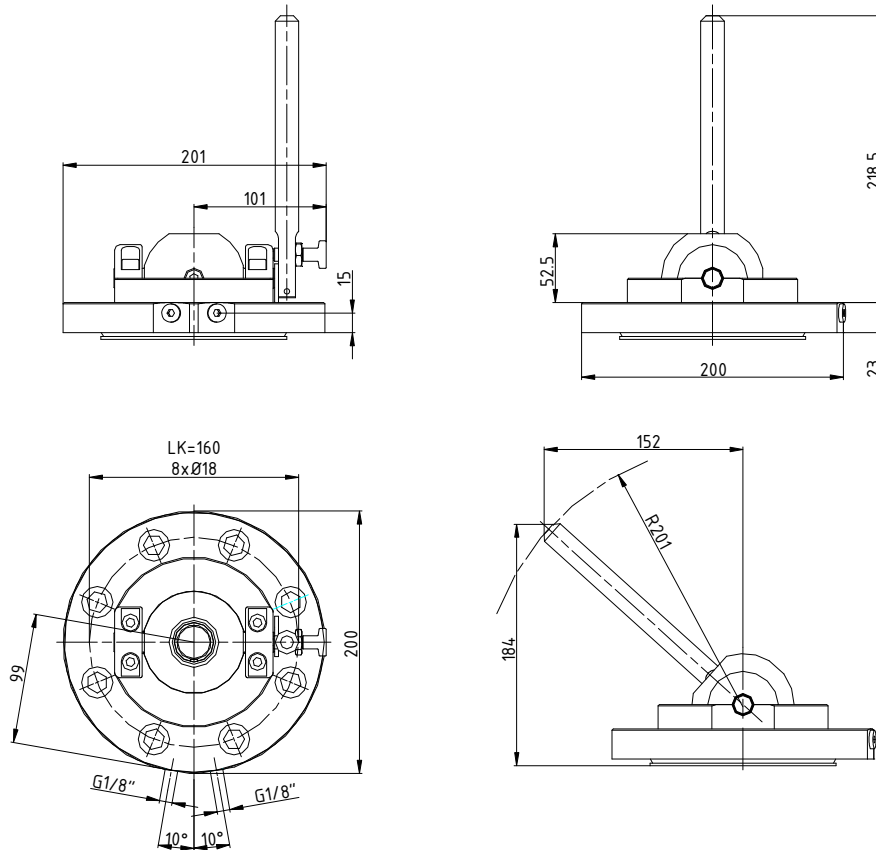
Abmessungen der Schwenkarmatur mit manuellem Schwenkhebel
